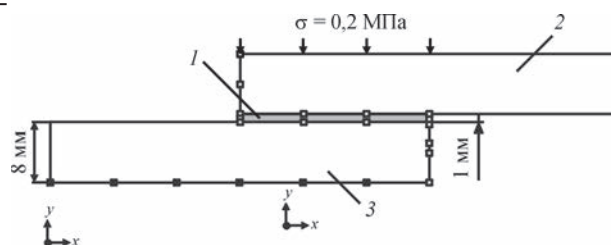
Схема двумерной модели нахлесточного соединения при сварке закладным элементом: 1 — закладной элемент; 2 — образец 1; 3 — образец 2
